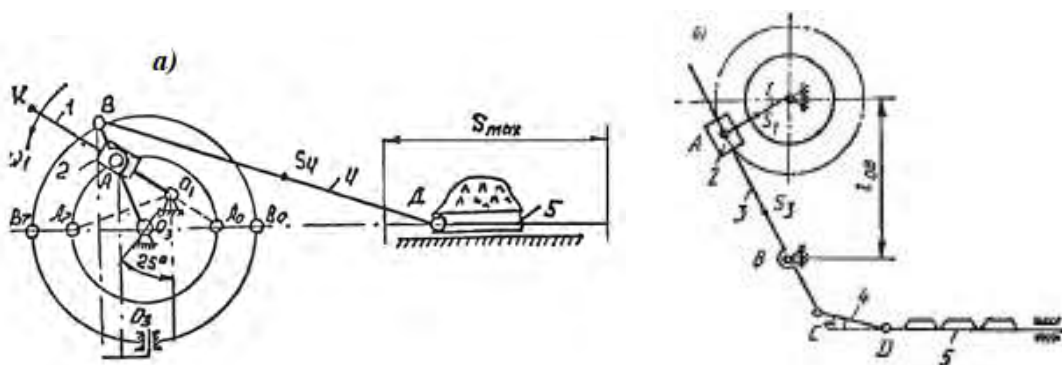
Кинематическая схема механизмов: а) грохота; б) валковой жатки
